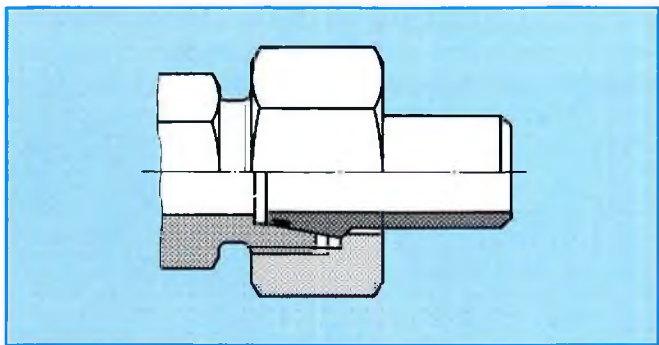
Резьбовое соединение с коническим штуцером под сварку с конусом по DIN 3865. Уплотнение: эластичное. Фиксация обеспечивается за счёт сварного шва.
